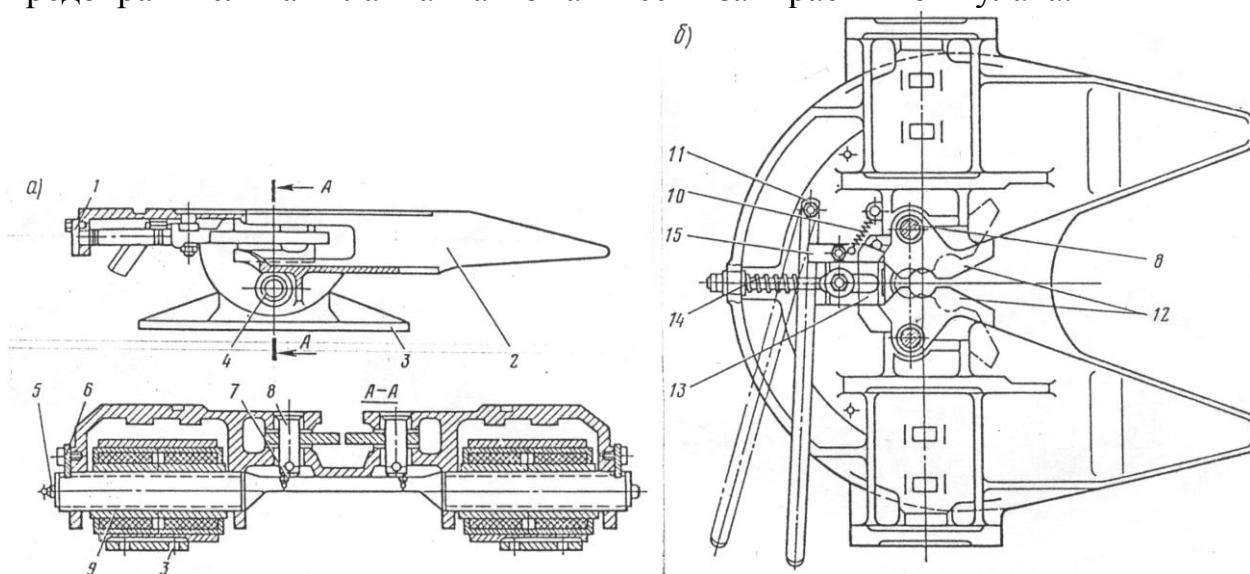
Седельно-сцепное устройство автомобиля-тягача МАЗ-504В: а – вид сбоку; б – вид сверху
